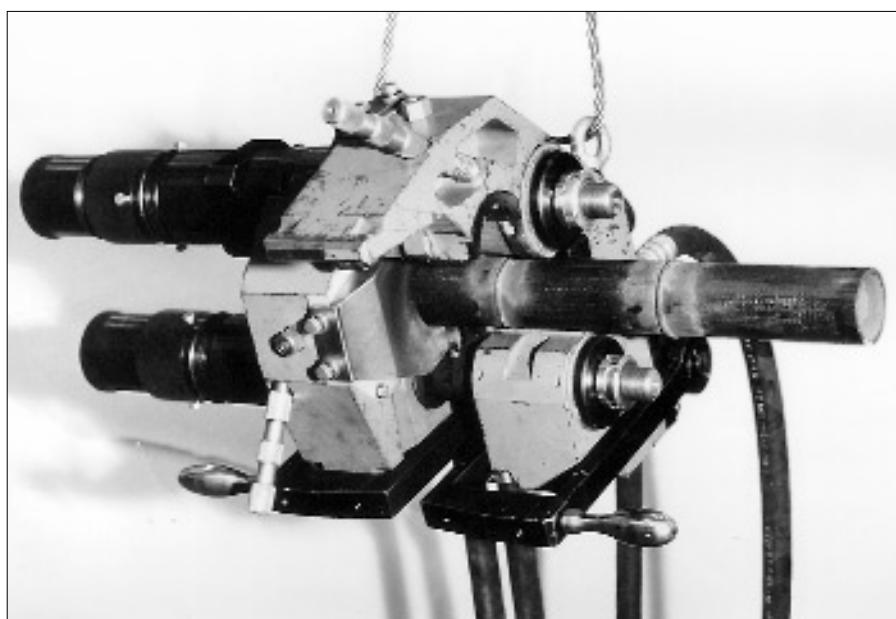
Модернизированная сварочная головка установки Об-2398
